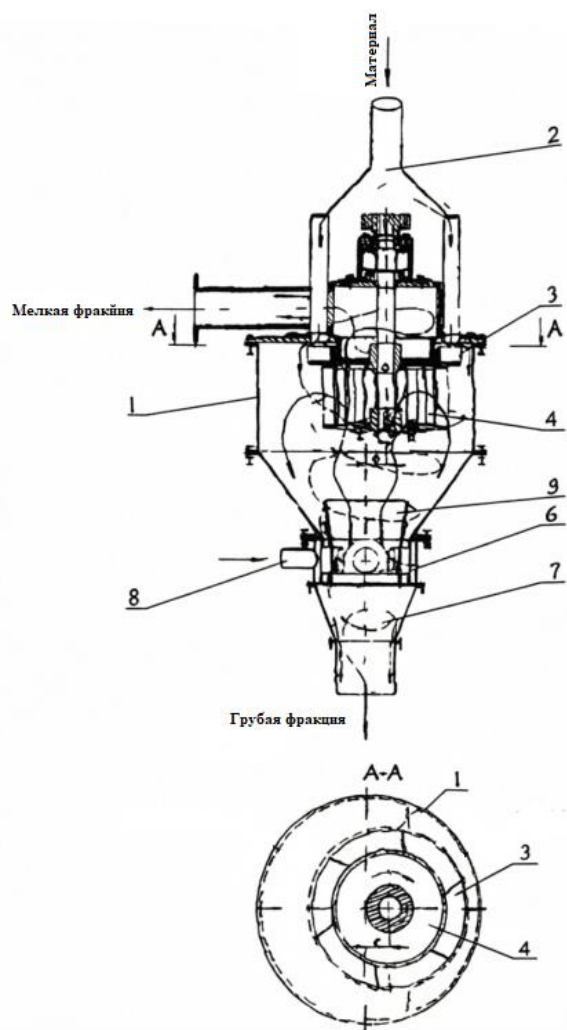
Схема центробежного сепаратора со смещенным ротором: 1 – корпус сепаратора, 2 – патрубок подачи исходного порошка, 3 – разбрасывающий диск, 4 – смещенный ротор, 5 – диффузор, 6 – коллектор продувочного воздуха, 7 – патрубок крупки, 8 – патрубок продувочного воздуха
